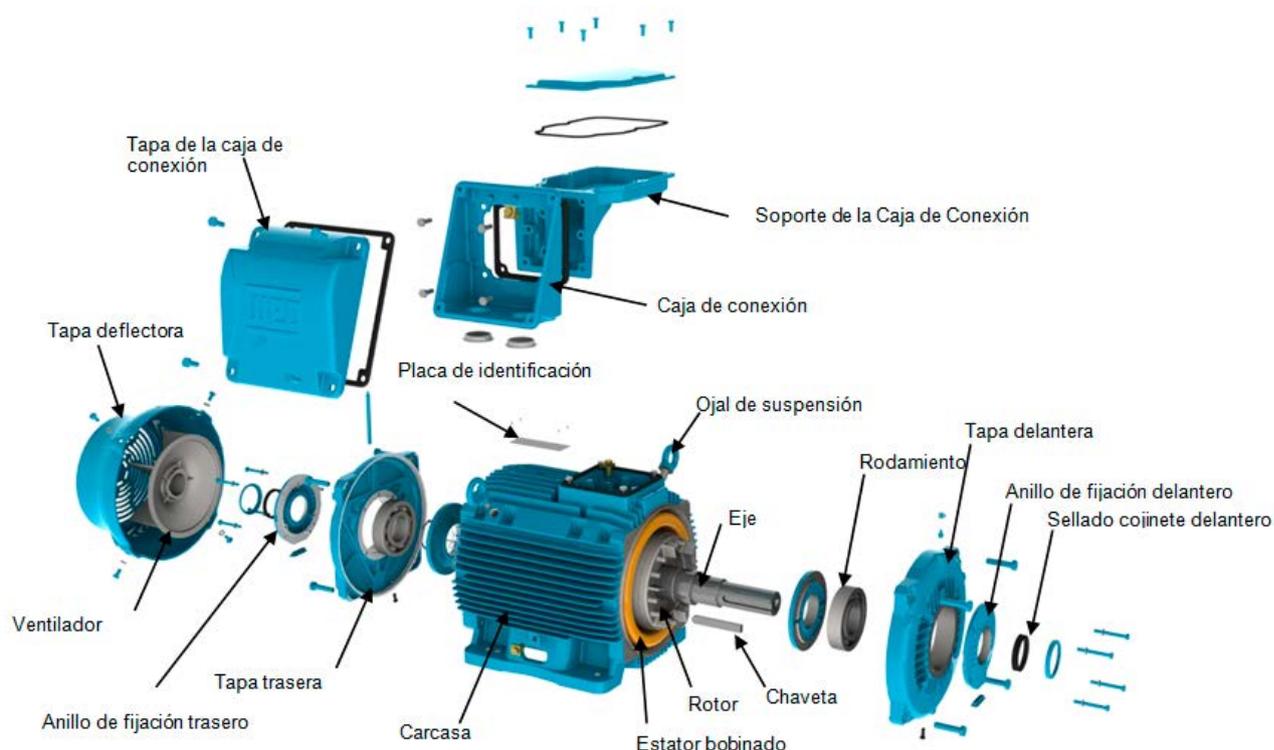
Vista explotada de los componentes de un motor W22.
